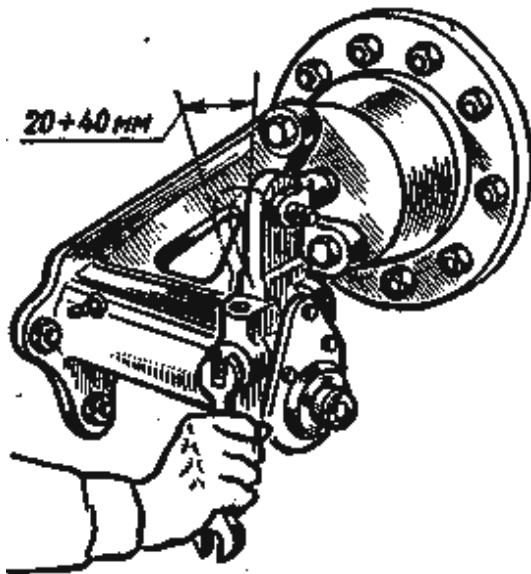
Регулювання колісних гальм, що мають пневматичний привід
